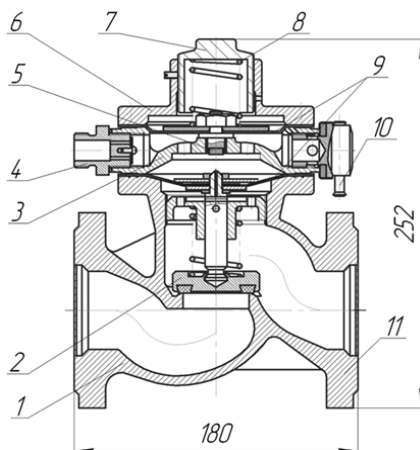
Клапан-отсекатель предохранительный ПКК-40М:
